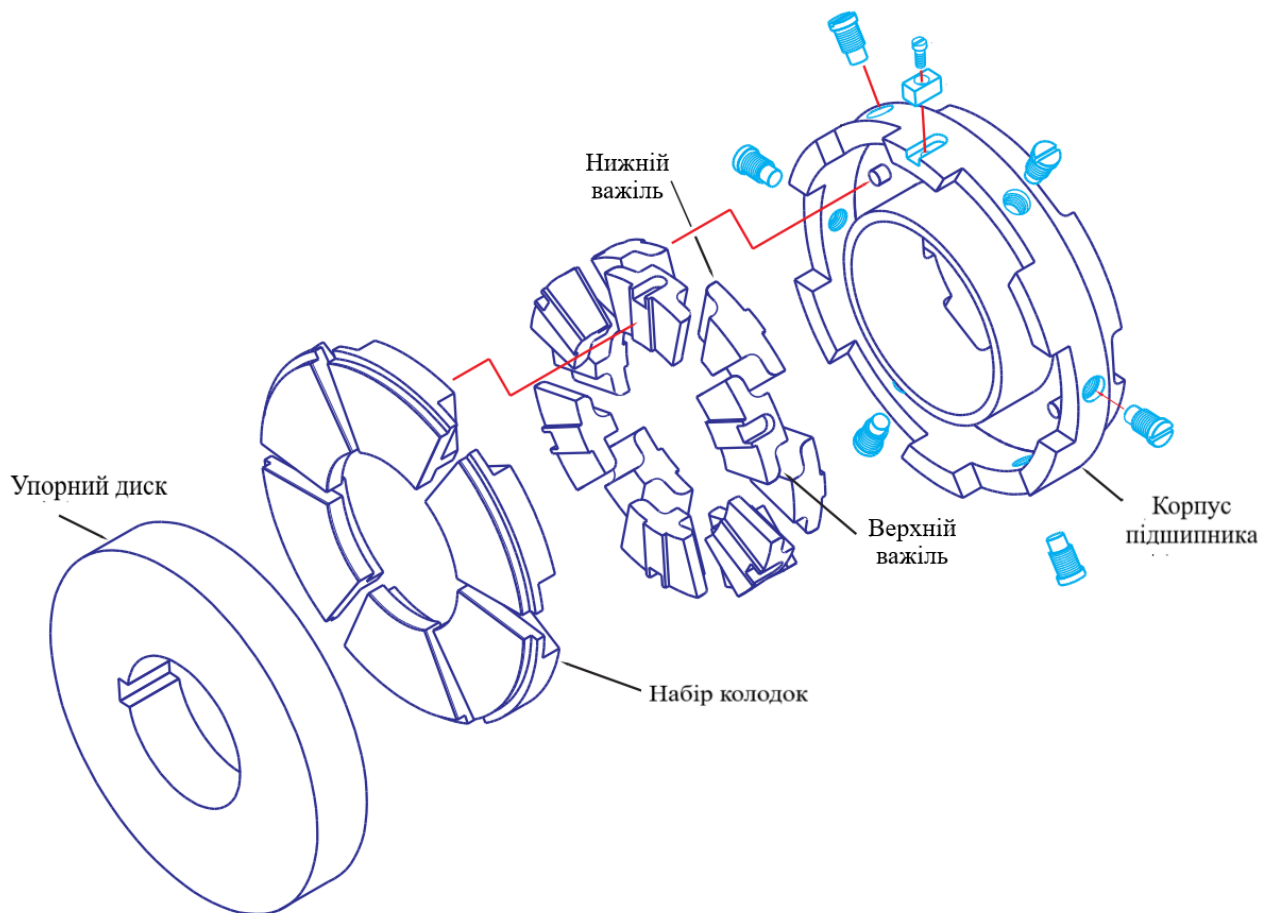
Схема упорного підшипника ковзання в розборі[3]
